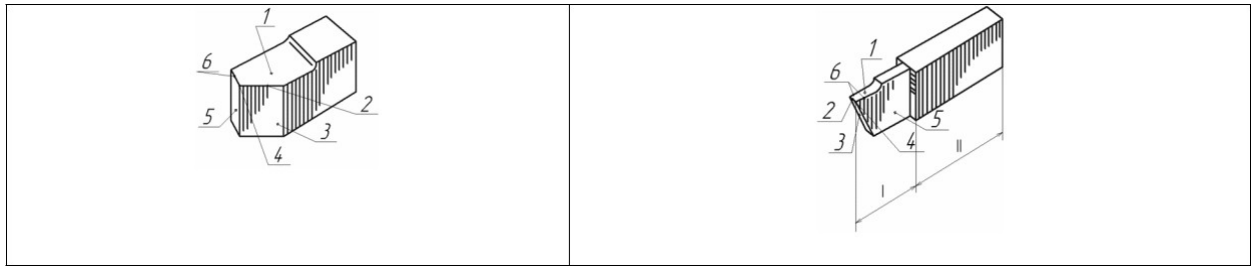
Элементы рабочей части токарного проходного резца: 1 – передняя поверхность; 2 – главная режущая кромка; 3 – главная задняя поверхность; 4 – вершина резца; 5 – вспомогательная задняя поверхность; 6 – вспомогательная режущая кромка
